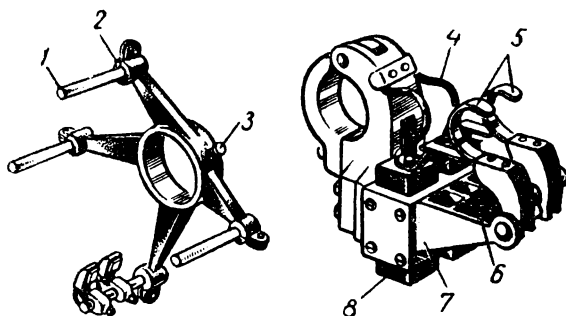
Траверса и щеткодержатель щеточного механизма:
